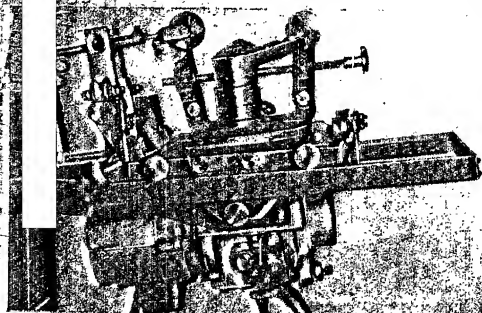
Нижняя сварочная головка автомата АРС-3
